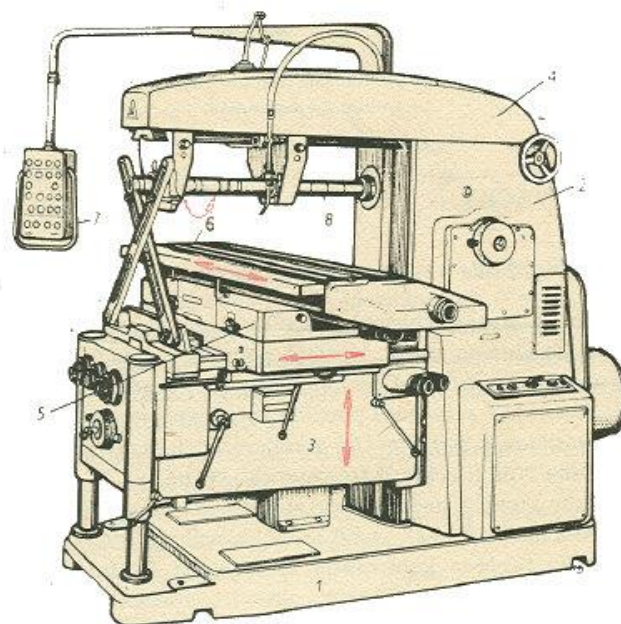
Konzolová frézovačka s univerzálnou hlavou
